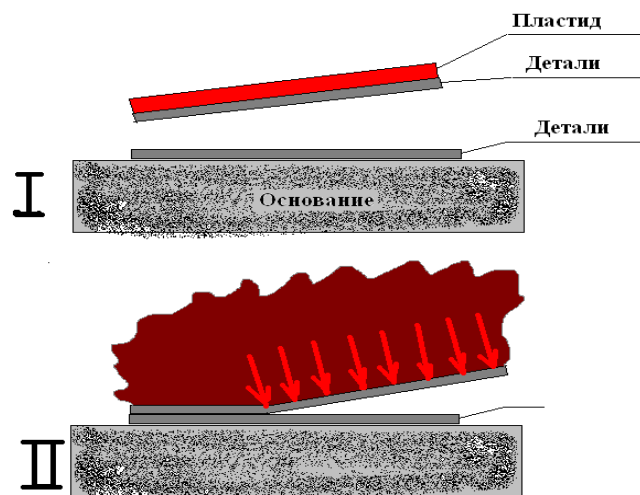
Схема кумулятивной сварки двух металлов
